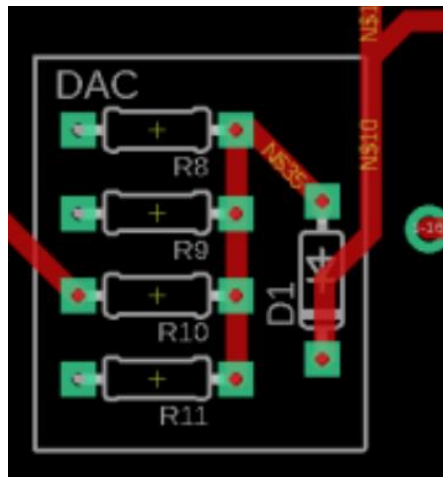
Disseny de la divisió DAC a la placa pilot d'en Marc Vigatà.
